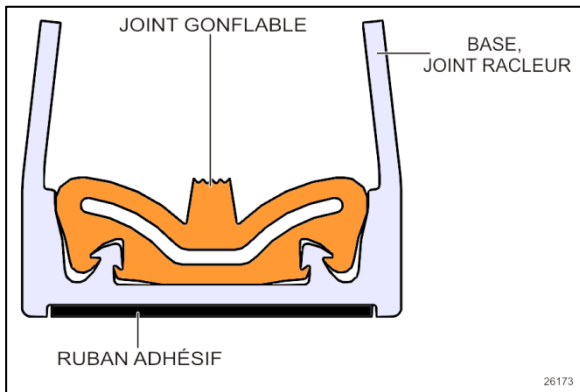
ENSEMBLE DE JOINT GONFLABLE DEUX PIÈCES
